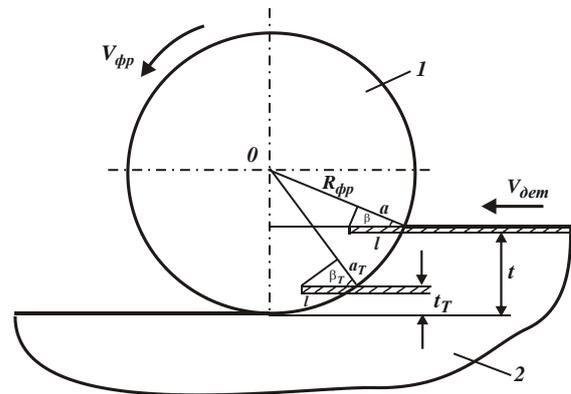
Расчетная схема параметров фрезерования цилиндрической фрезой:
